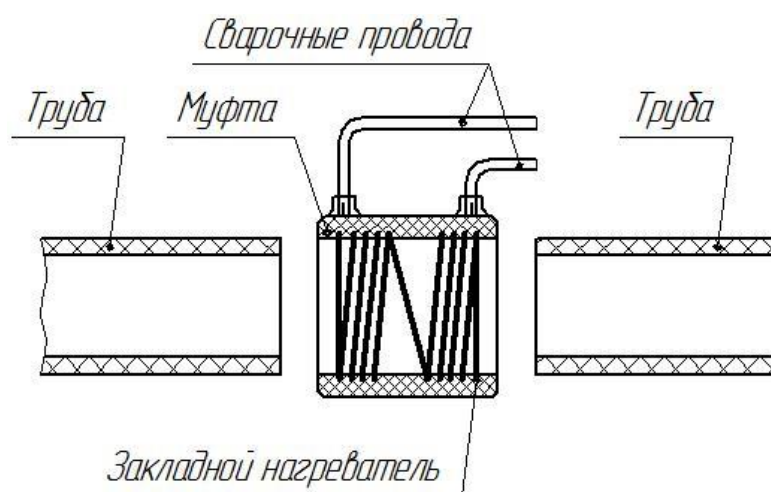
Схема сварки электрическими муфтами
